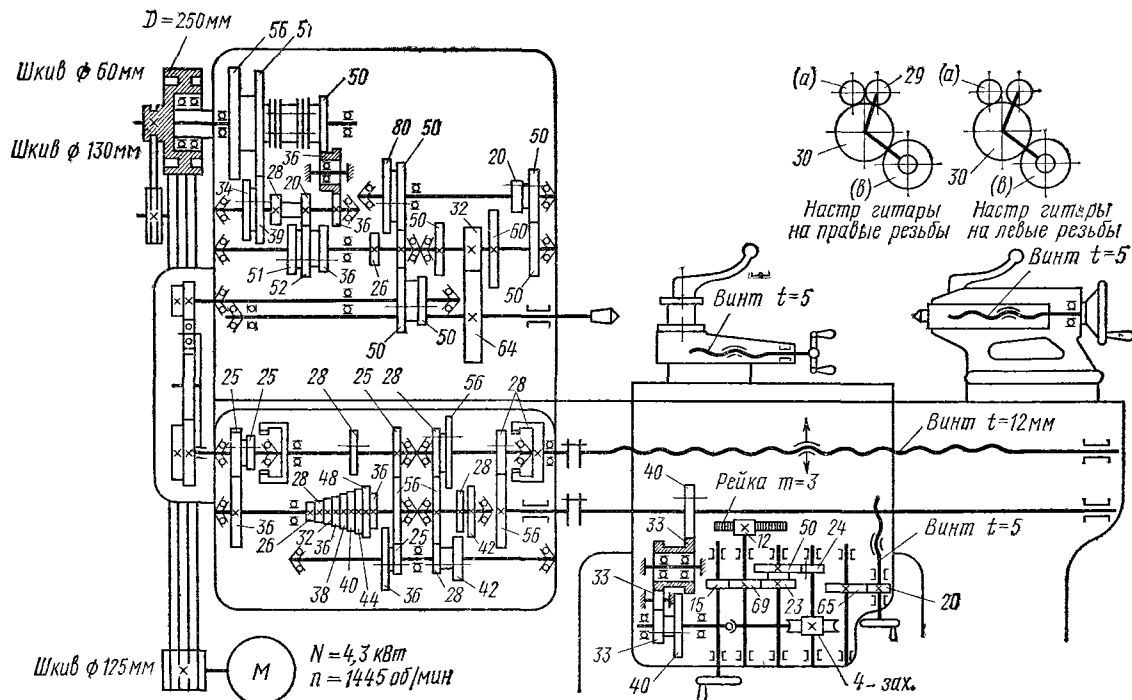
Кинематическая схема станка 1Д62 (цифрами обозначены числа зубьев)
